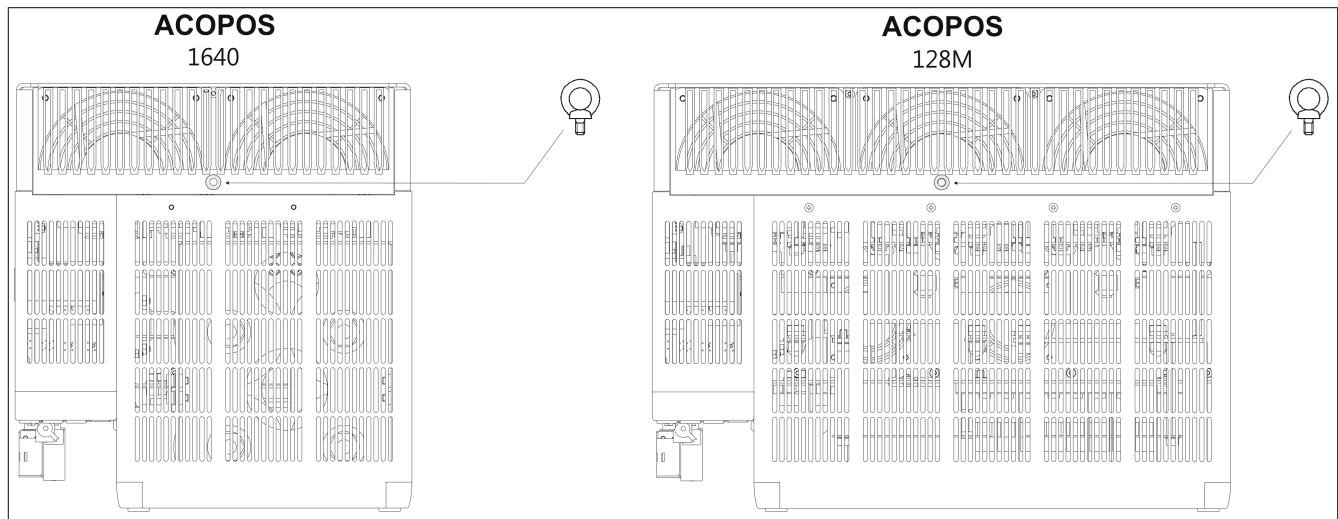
Montageposition der Ringschraube zum Anheben von ACOPOS 1640, 128M
